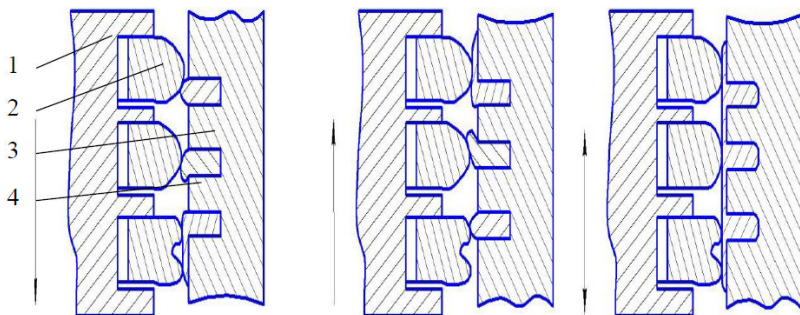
Схема образования плёнки на поверхности гильзы цилиндров: 1-поршень; 2-поршневое кольцо; 3-гильза цилиндров; 4-вставка
